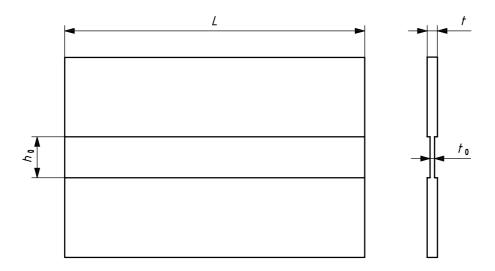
Форма образца испытания на чистый срез для измерений скорости роста усталостной трещины
